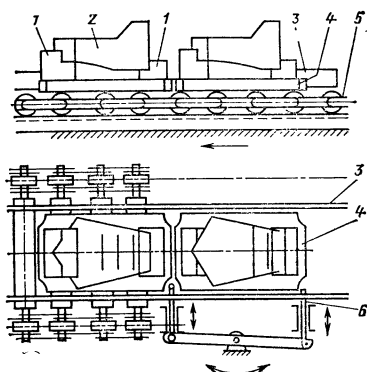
Транспортные приспособления-спутники на цепном роликовом транспортере
